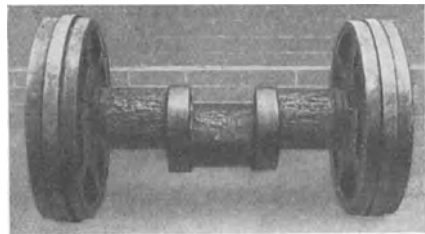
Abgelaufene, durch Aufschweißen reparierte Kurbelwelle.
